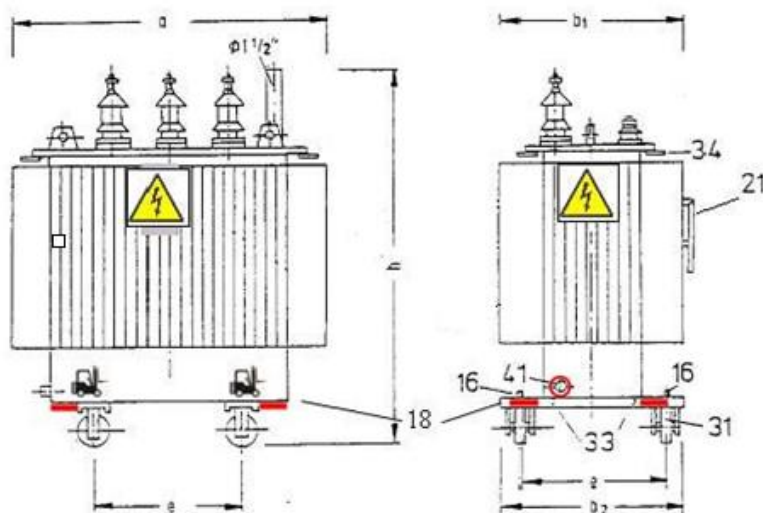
Angeschweißte Metallplatte zur Kippsicherung (Bild 9, Detail 18)
